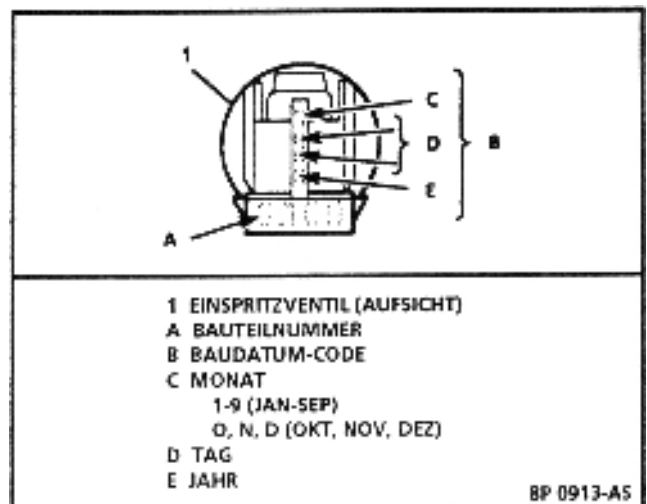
Lage der Bauteilnummer am Einspritzventil
